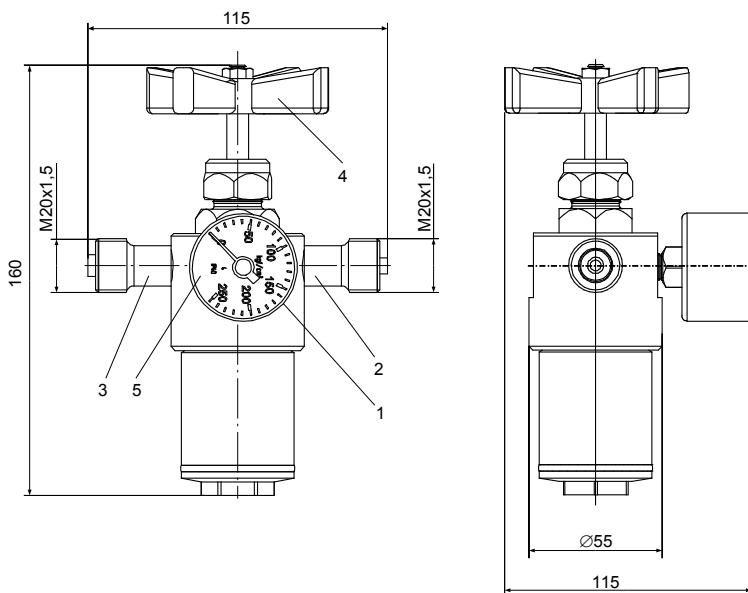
Габаритные и присоединительные размеры ФДУ: 1 – корпус; 2 – штуцер входной; 3 – штуцер выходной; 4 – винт регулировочный; 5 – манометр.
